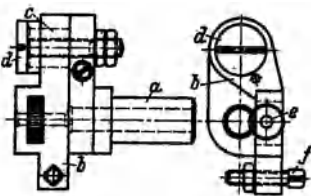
Schwenkbarer Rändelhalter. *a* Halterkörper mit Schaft; *b* Rändelträger, um Zapfen *c* schwenkbar; *d* Halteschraube für Teil *b*; *e* Rändel; *f* Druckschraube zum Eindringen des Rändels durch eine entsprechende Leiste am Querschlitten.
